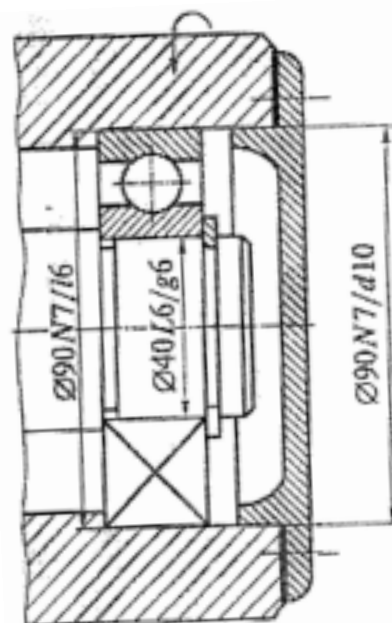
Обозначение посадок в подшипниковых узлах.
